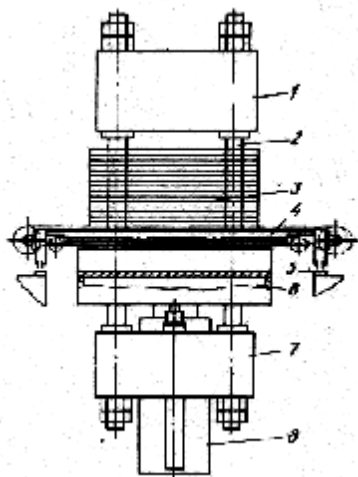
Пресс П714Б, реконструированный под подпрессовку: 1 - архитрав, 2 - колонна, 3 - пакет для подпрессовки, 4 - загрузочный конвейер, 5 - упор регулирования уровня загрузки, 6 - подъемный стол, 7 - основание, 8 - гидроцилиндр.
